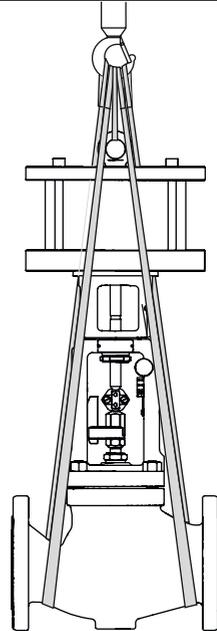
Ringschraubenabdeckung geschlossen
